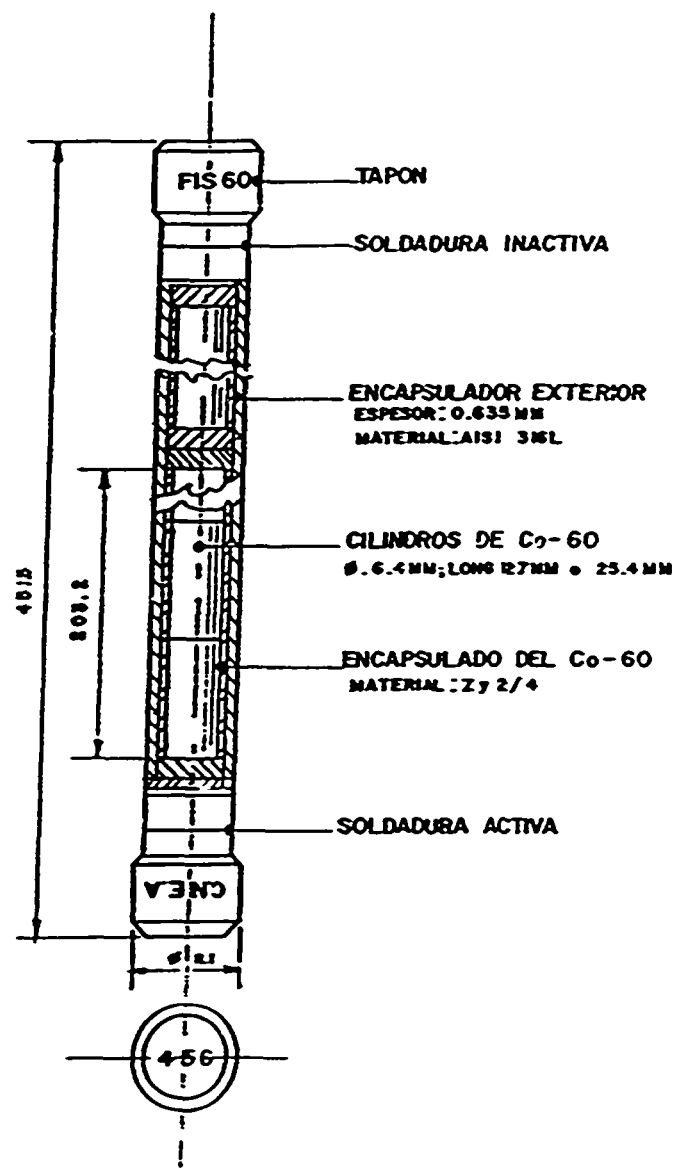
Corte de un lapiz de Co-60, se muestran las diferentes partes que lo componen.
